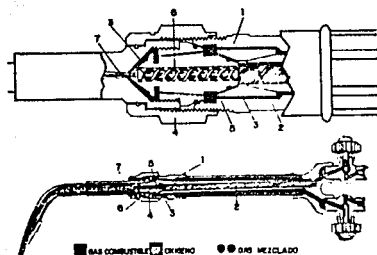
Detalles del soplete para oxiacetileno.- 1, cabazal del soplete; 2, tubo de oxígeno; 3, paso para el acetileno; 4, tuerca de la boquilla; 5, extremo terminal del cono de la boquilla de soldar; 6, mezclador espiral en la boquilla de soldar; 7, orificio del mezclador espiral y cámara mezcladora.
